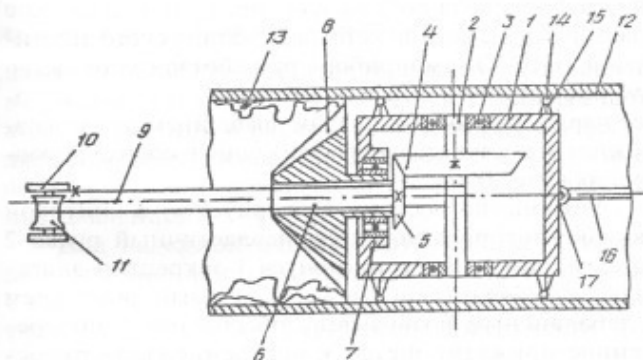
Очистное устройство для поэтапной чистки внутренней поверхности трубопровода от твердых отложений, где 1 – корпус; 2 – ведущий вал; 3 – подшипник; 4 – ведущая шестерня; 5 – коническая шестерня; 6 – пустотелый вал; 7 – подшипник; 8 – фреза; 9 – приводной трос; 10 – лебедка; 11 – барабан; 12 – очищаемый трубопровод; 13 – твердые отложения; 14 – центровочные ролики; 15 – пружины; 16 – аварийный трос; 17 – пружина.
